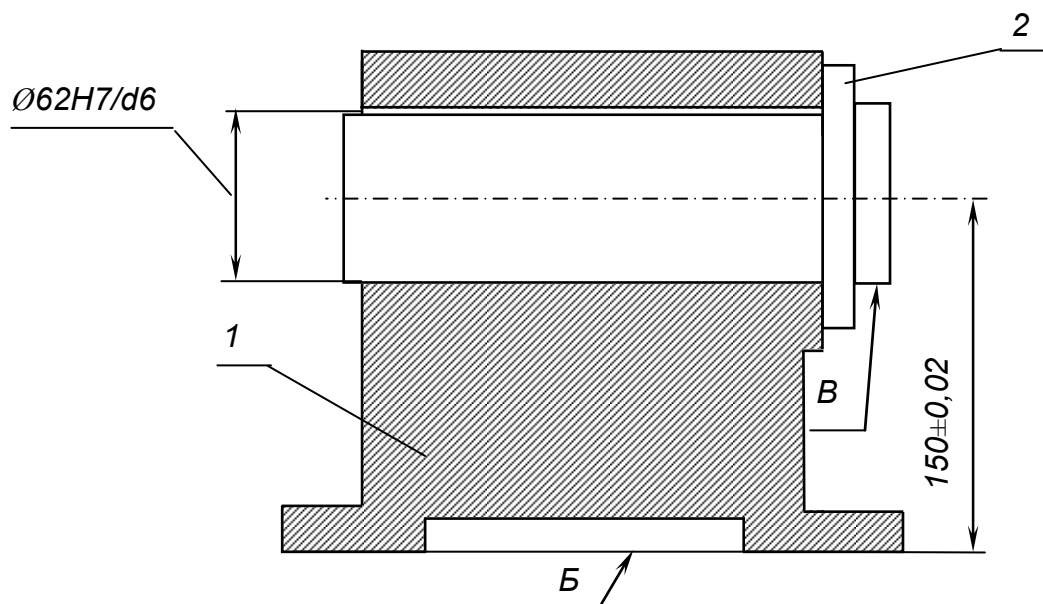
Конструктивна схема шпиндельного вузла
